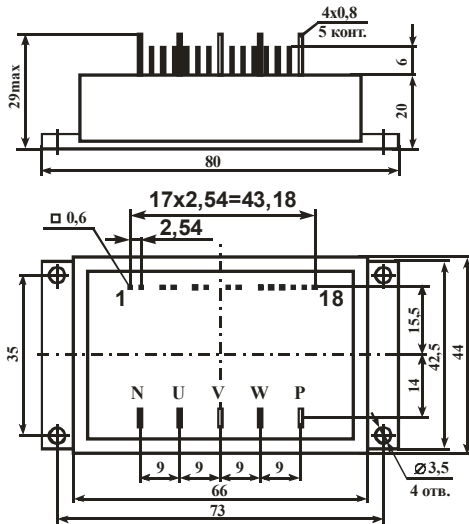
Габаритный чертеж модулей M13MA-10-6
